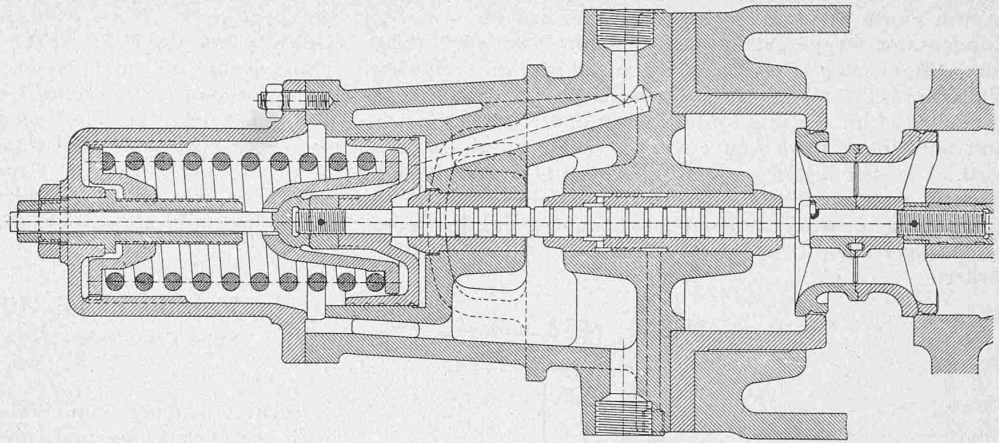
Doppelsitzventil einer Düsengruppe mit Druckölsteuerung der Tosi-Dampfturbine.
